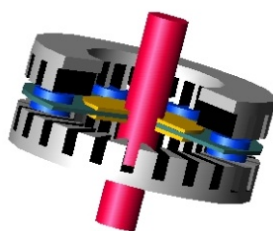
Desenho do motor em disco usando rotor com materiais SAT [Bondrea].
